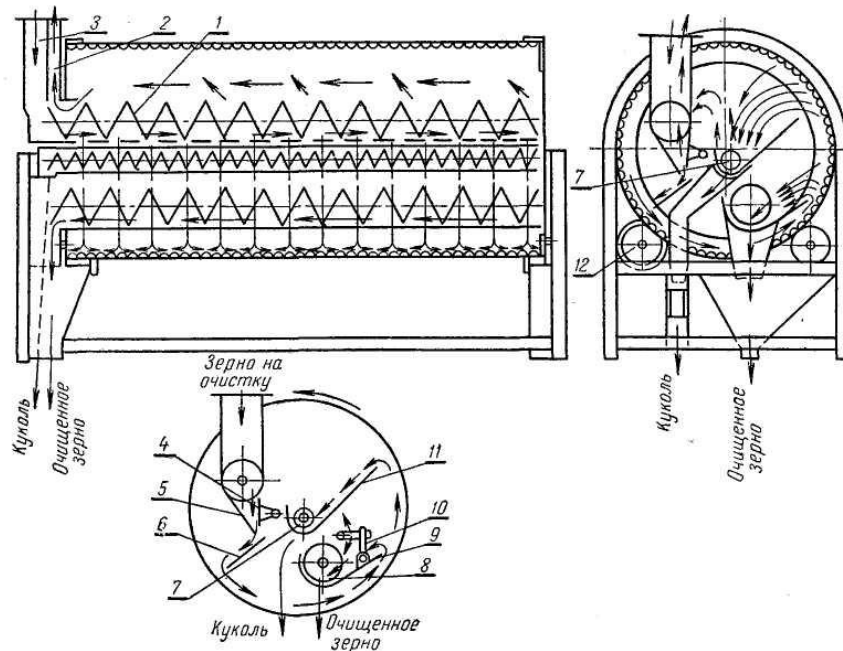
Циліндричний трієр для відбору коротких домішок
